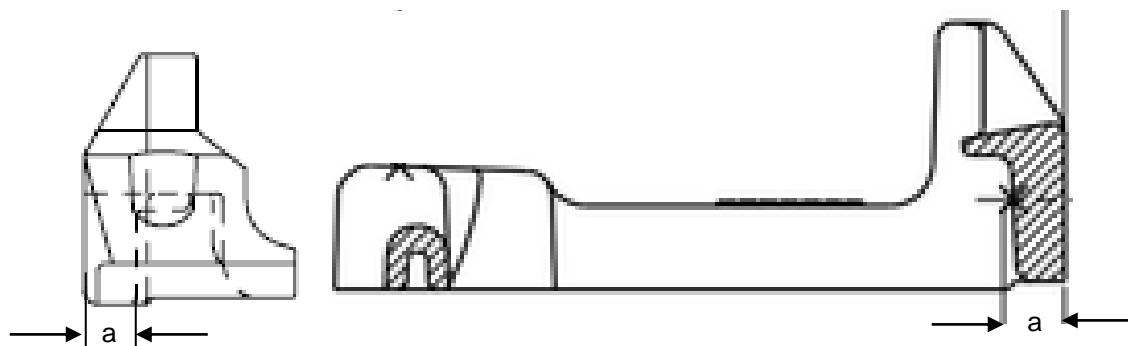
Поперечный разрез боковых изоляторов для крепления Fastclip (Pandrol)
